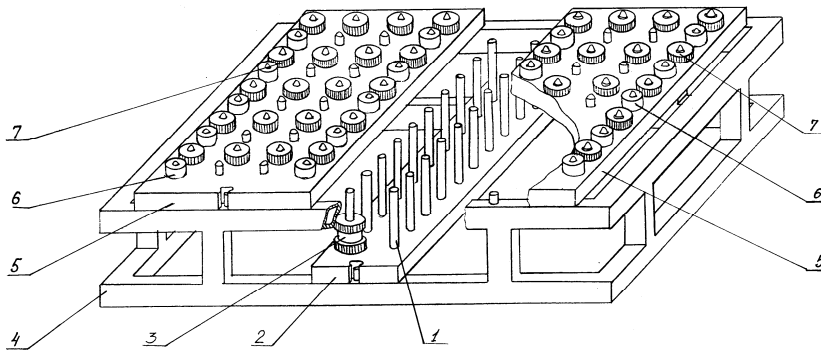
Схема расположения на палетах деталей для сборки ротора шагового двигателя ДШИ-200-1:
